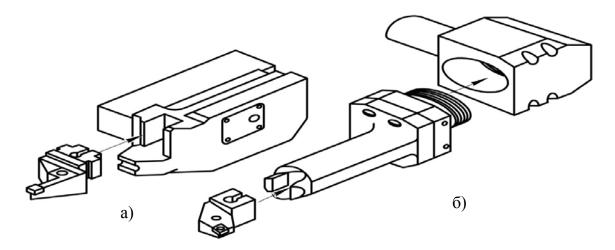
Оправки и вспомогательные блоки для модульного режущего инструмента: a - для суппорта; б - для револьверной головки
